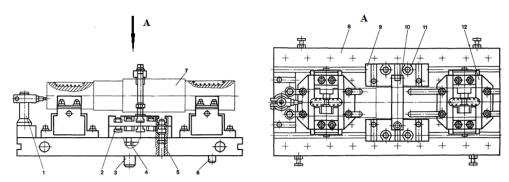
Приспособление для установки вала: I – опора; 2, 3 - пальцы базирующие; 4 - болт станочный, 5, 6 - пальцы базирующие; 7 - заготовка, 8 - плита, 9 - планка, 10 – прижим; 11 – гайка; 12 - призма
